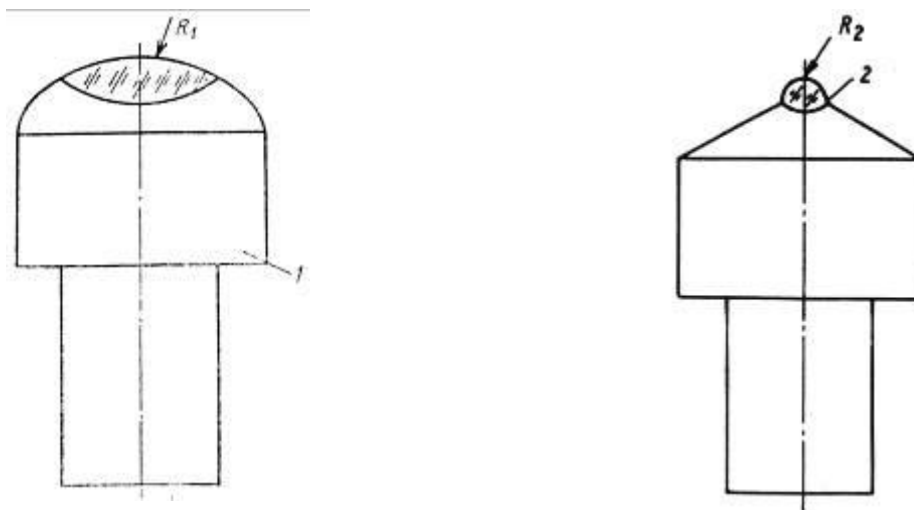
Инструмент с рабочей поверхностью, образованной цилиндрами разного радиуса
